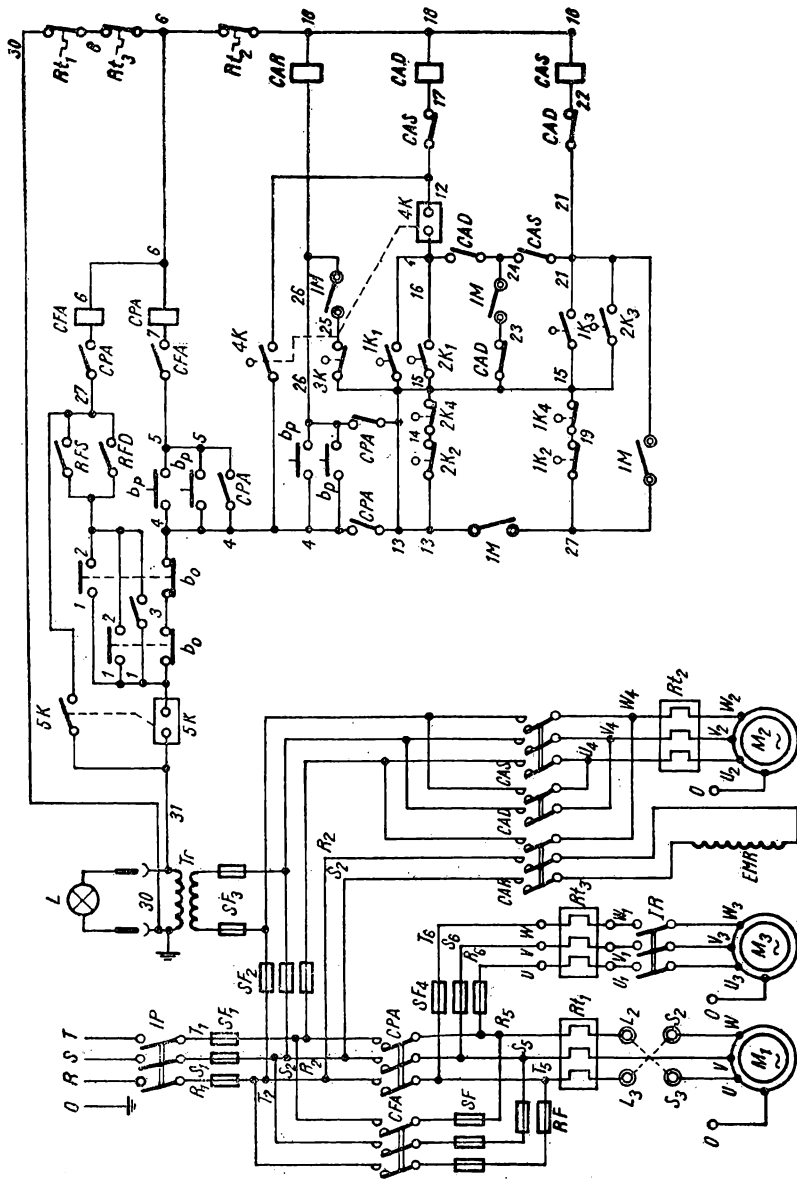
Schema electrică a mașinii universale de frezat FU 32.
